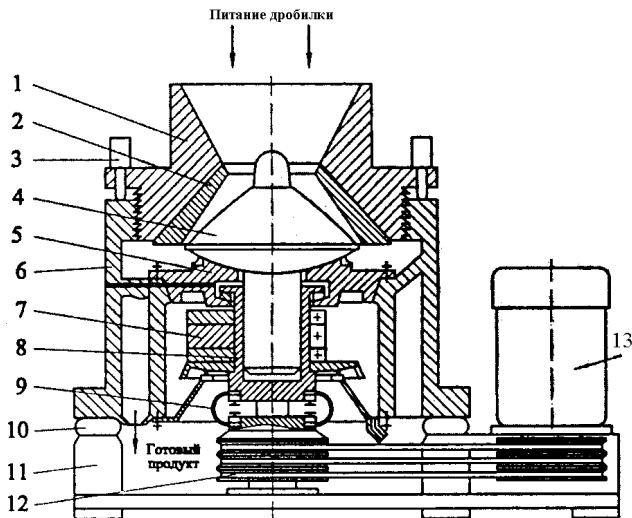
Виброконусная дробилка: 1 – наружный конус; 2 – броня наружного конуса; 3 – гидродомкрат; 4 – внутренний конус; 5 – сферическая опора; 6 – корпус; 7 – неуравновешенный ротор-вибратор; 8 – подшипник ротора-вибратора; 9 – эластичная муфта; 10 – резиновые амортизаторы; 11 – металлическая опора; 12 – клиноременная передача; 13 – электродвигатель.
